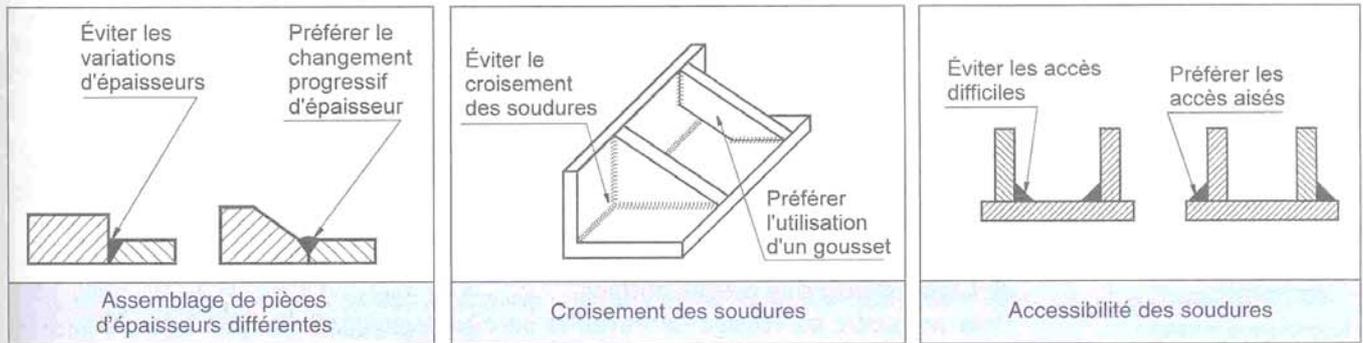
Exemples d'assemblage par soudage.
